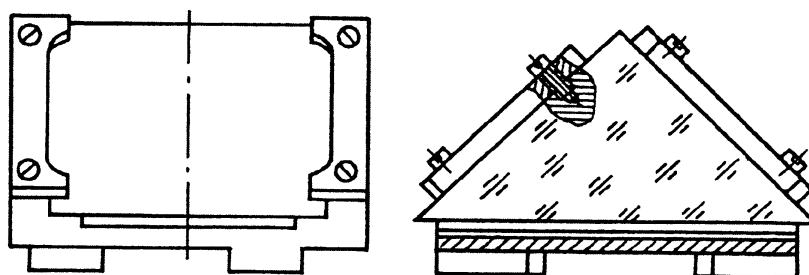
Крепление призмы BP-180 прижимными планками
